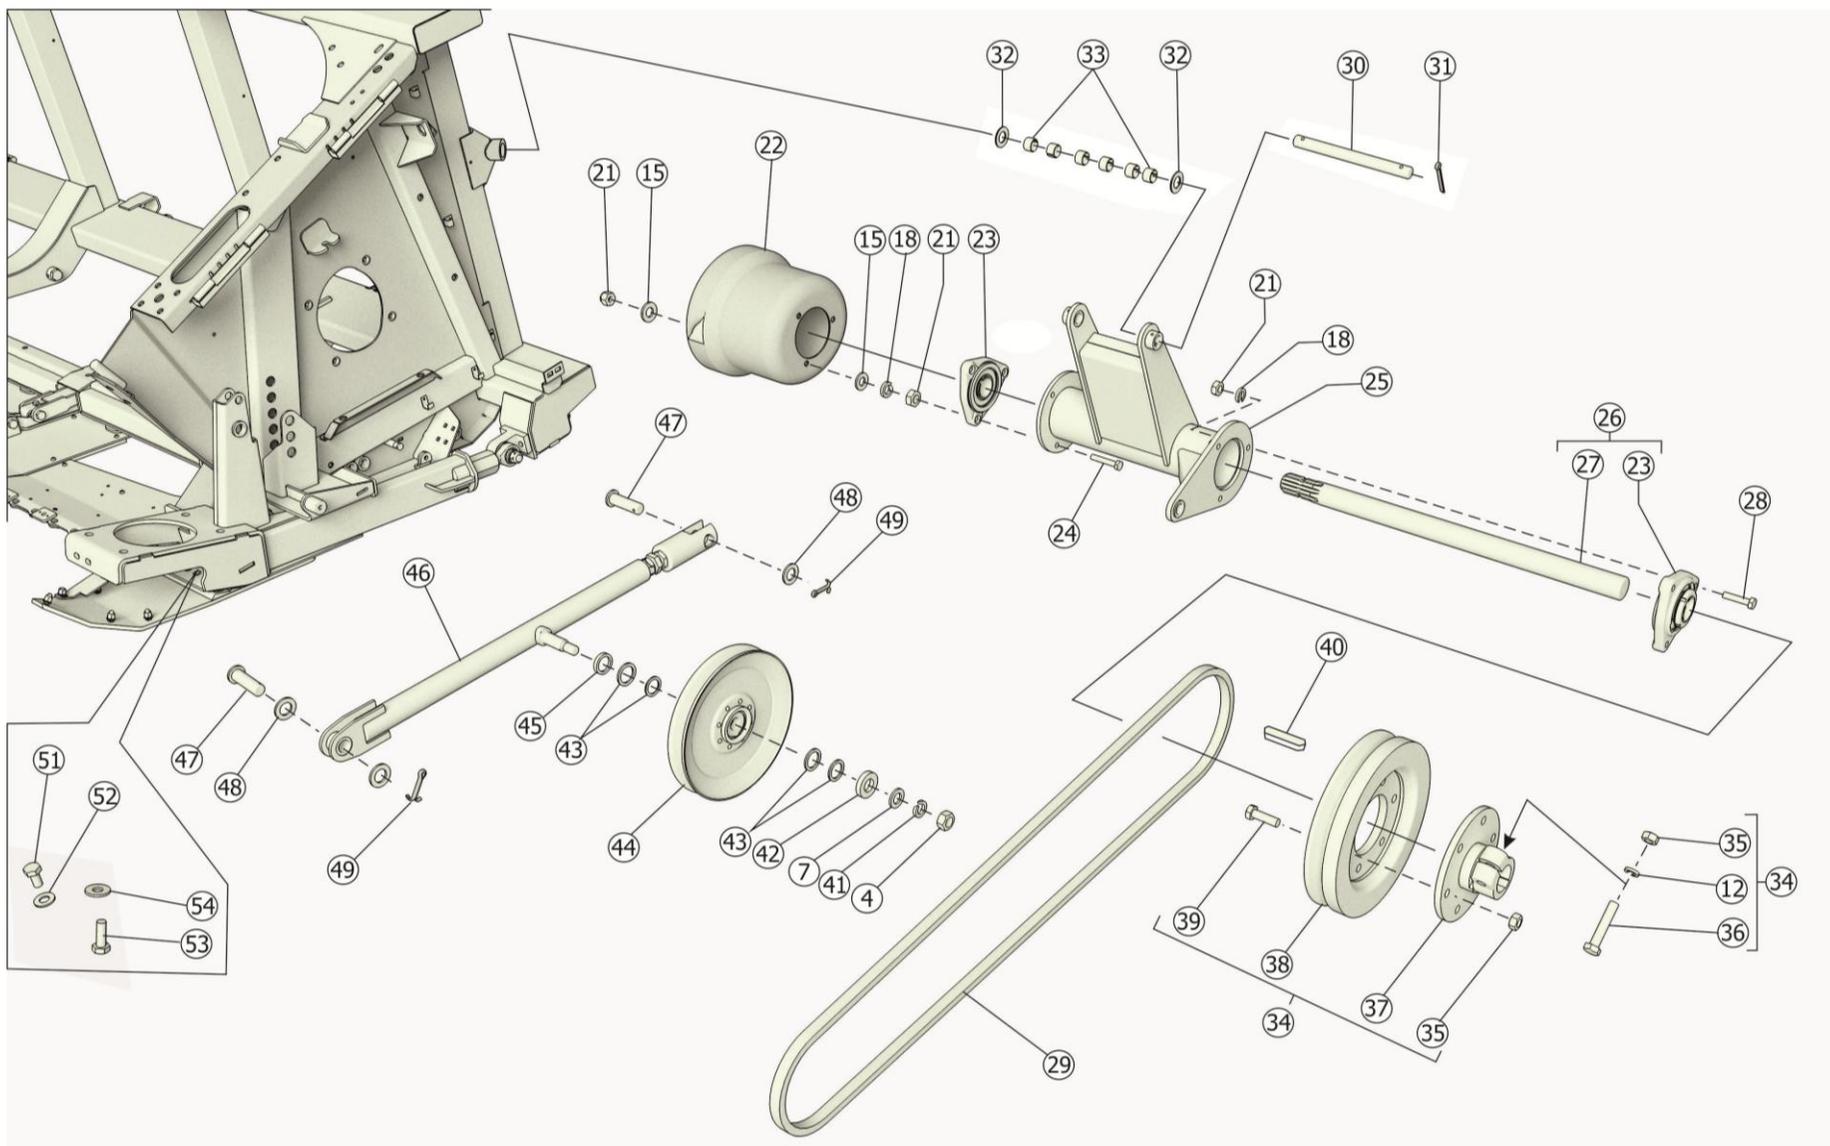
Привод режущего аппарата ЖСУ-703.01.03.500Б
